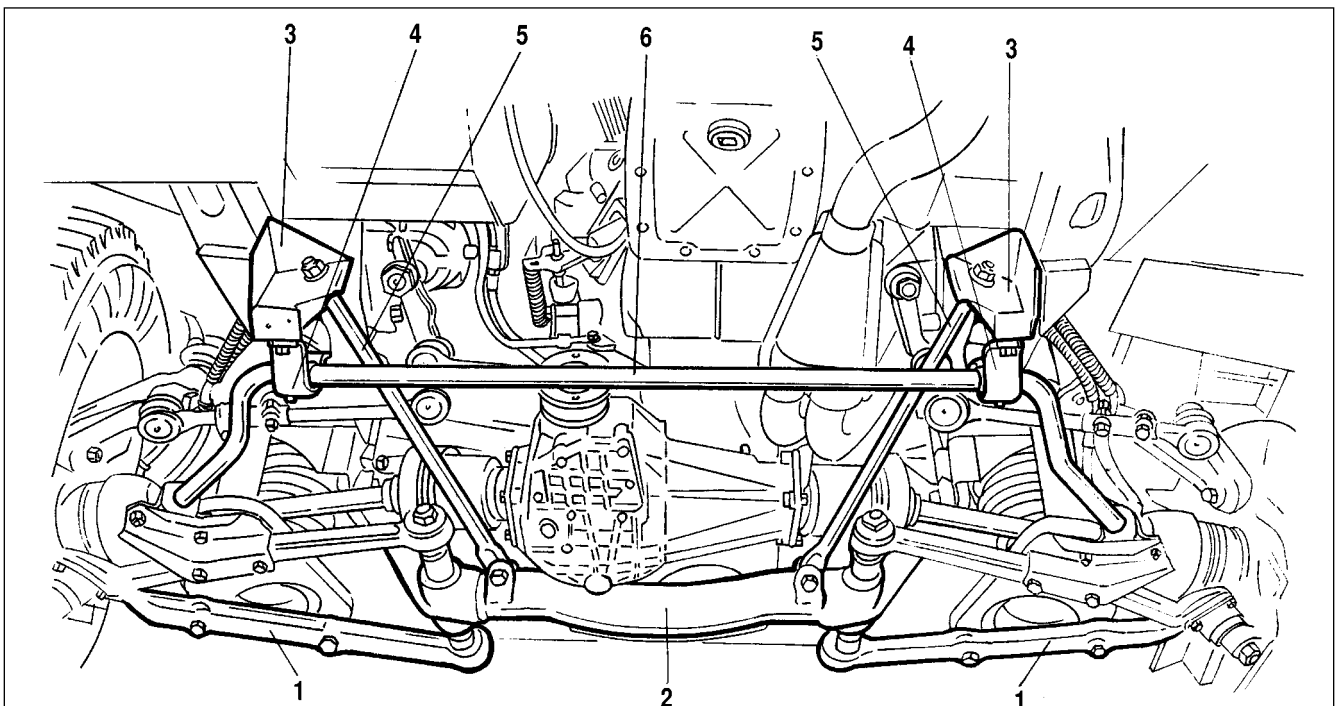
Eingebaute am Fahrzeug Vorderradaufhängung (Rückansicht):
